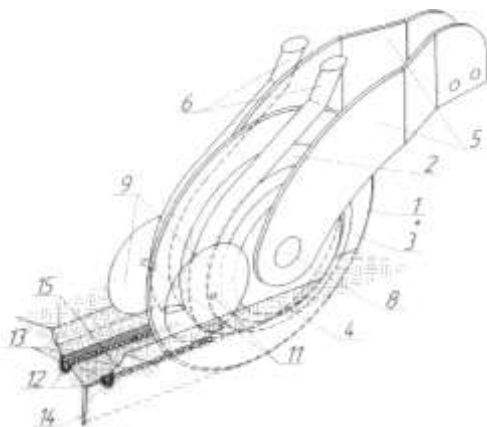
Технологическая схема работы комбинированного однодискового сошника с двухсторонними ребрами и дисковыми загорточами: 1 – плоский диск; 2 – внутренняя ребра; 3 – бороздкообразователь; 4 – наружная ребра; 5 – корпус; 6 – семянаправители; 8, 11 – оси; 9 – сферические диски; 12 – ложа; 13 – семена; 14 – щель; 15 – бороздки
